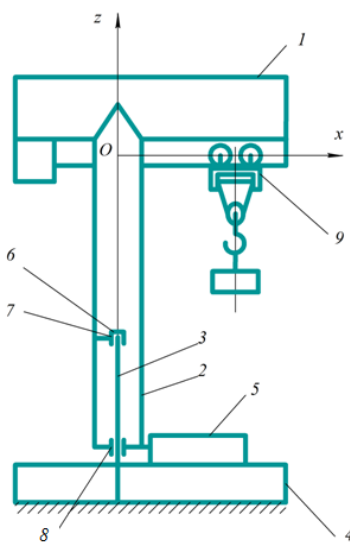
Кинематическая схема консольного крана на колонне: 1 – стрела; 2 – гильза; 3 – колонна; 4 – опорная рама; 5 – механизм поворота; 6, 7, 8 – подшипники; 9 – тележка
